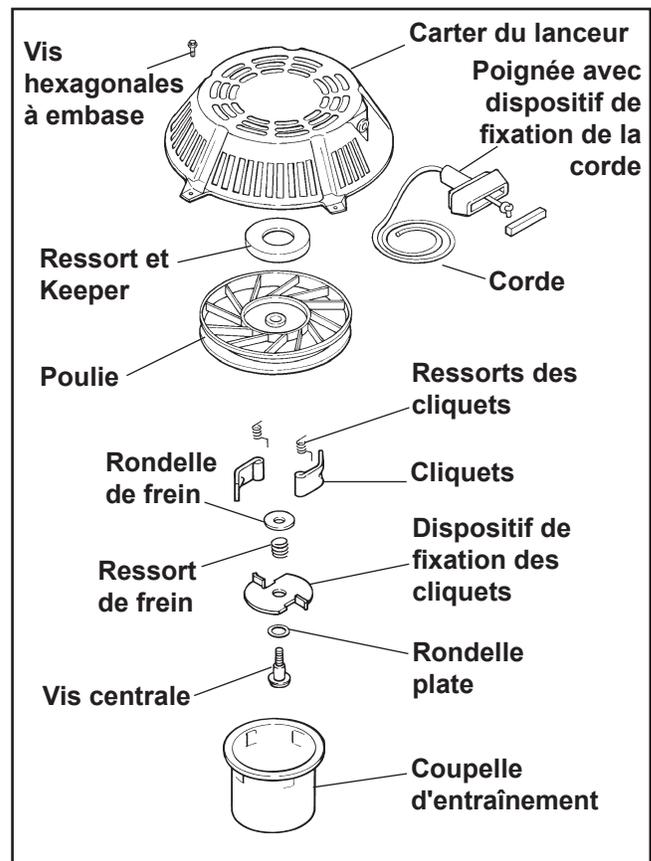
Lanceur à enroulement automatique - Vue éclatée.
